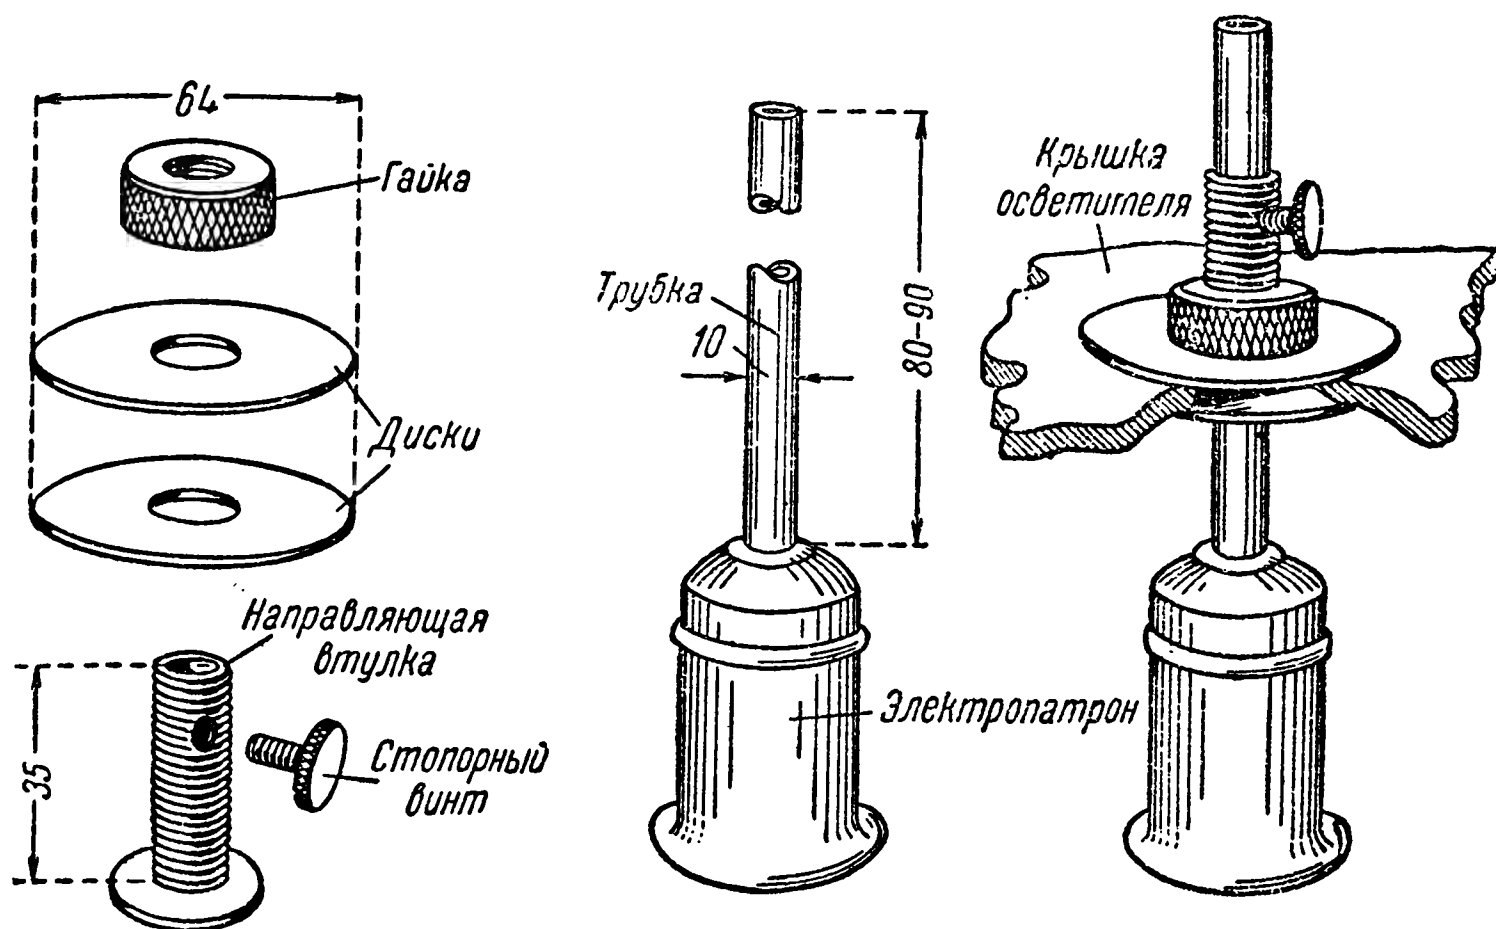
Детали центрирующего устройства и устройство в собранном виде
